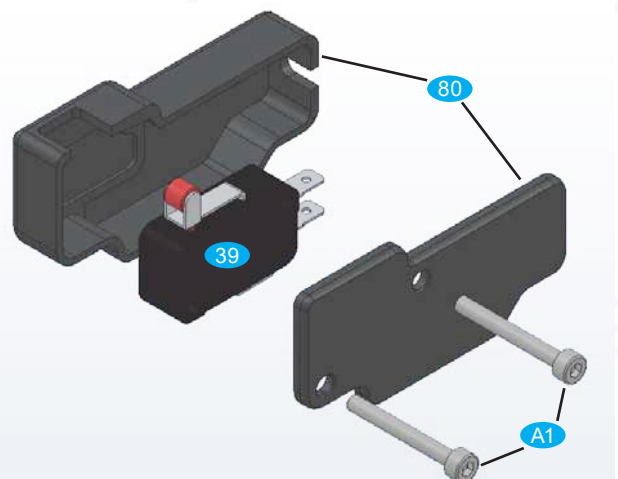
Baugruppe Referenzschalter / Gehäuse.
